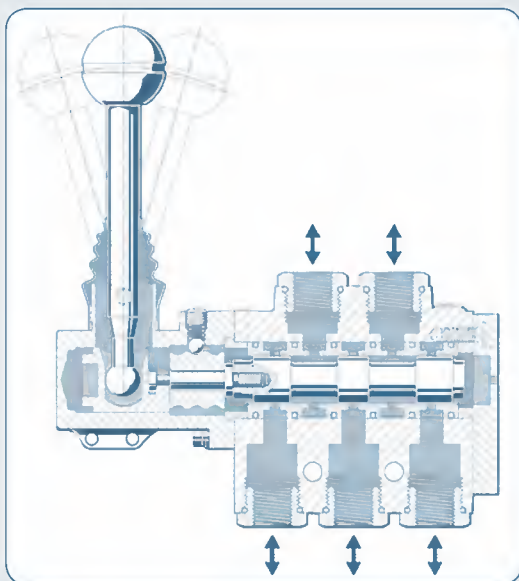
Blick ins Innere mit der Schnittzeichnung
